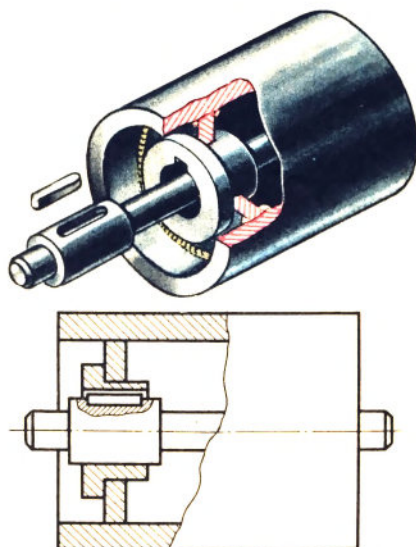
Чертеж сварного изделия в соединении с другими деталями
